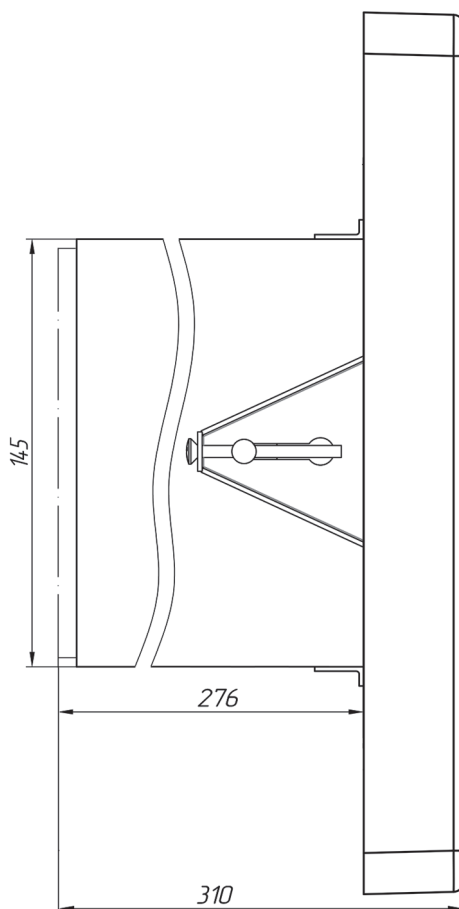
Вид сбоку контроллера БАЗИС-21.3
